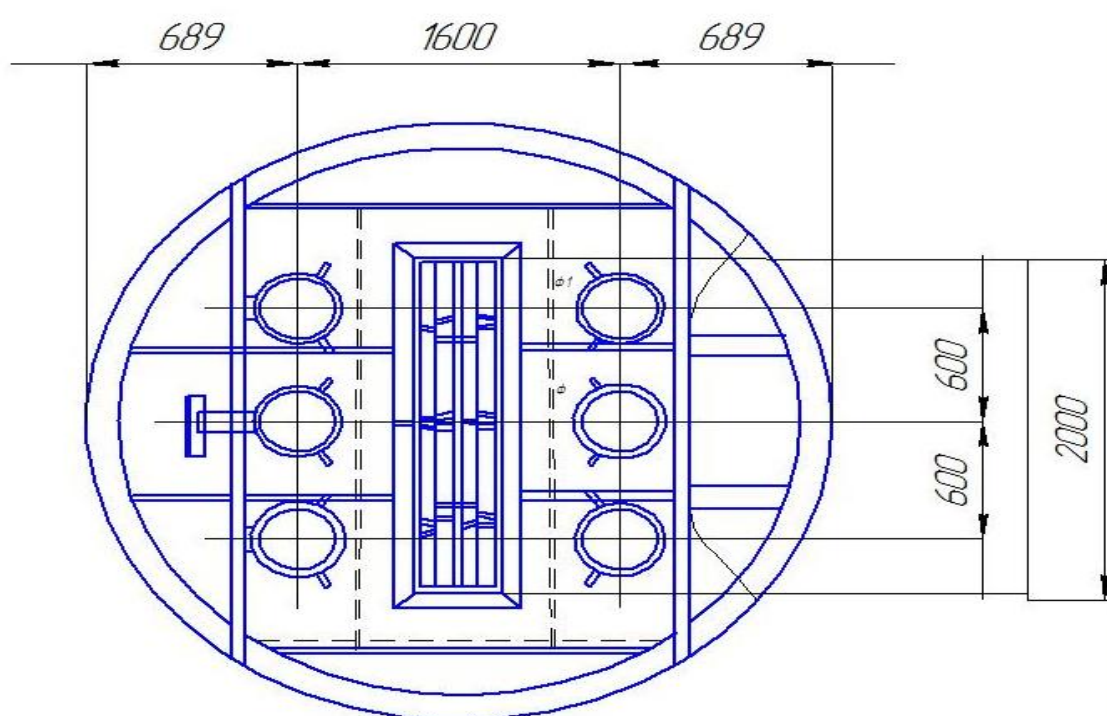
Чертеж вид сверху - в разрезе [44]
